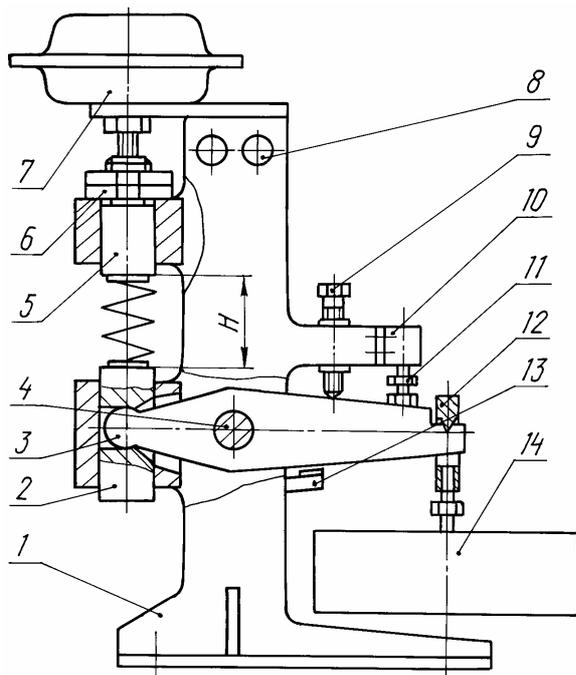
Стенд для контроля жесткости пружин: 1 – корпус; 2, 5 – скалки; 3 – рычаг; 4 – ось; 6 – гайки регулировочные; 7 – пневмокамера; 8 – световой индикатор; 9 и 11 – болты регулировочные; 10 – конечный выключатель; 12 – призма; 13 – упор; 14 – груз
